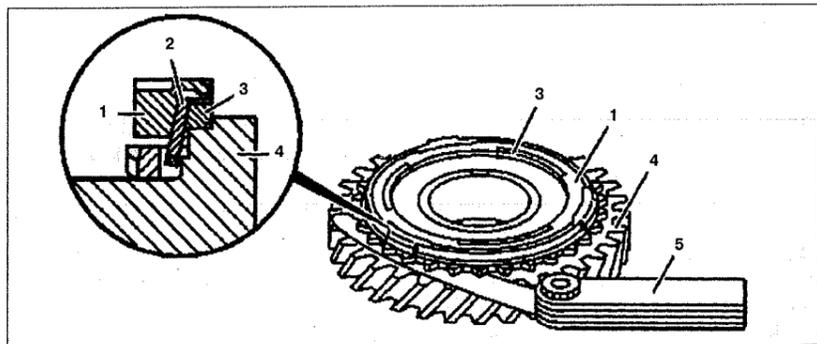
Проверка износа между кольцами синхронизатора и корпусом муфты (автомобили с двигателями 111.948 и 601.970):
